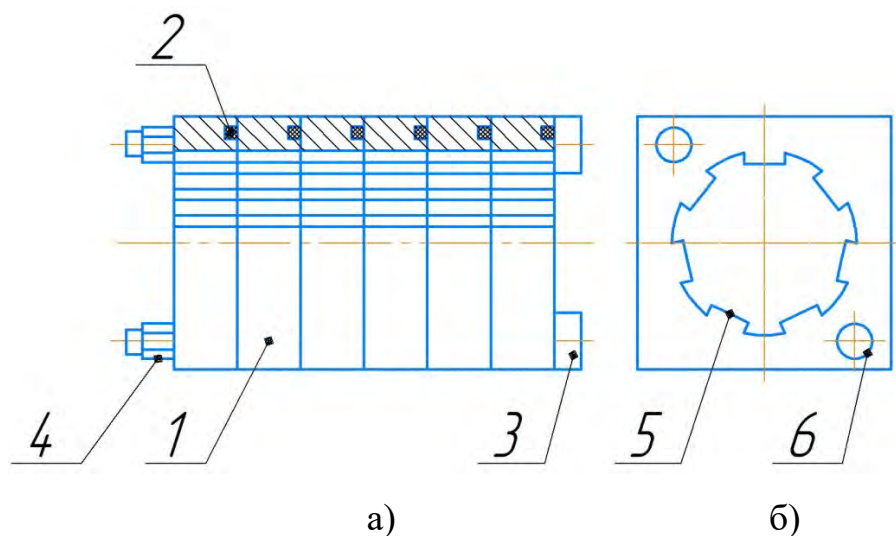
Устрій робочого циліндру збірної конструкції:
